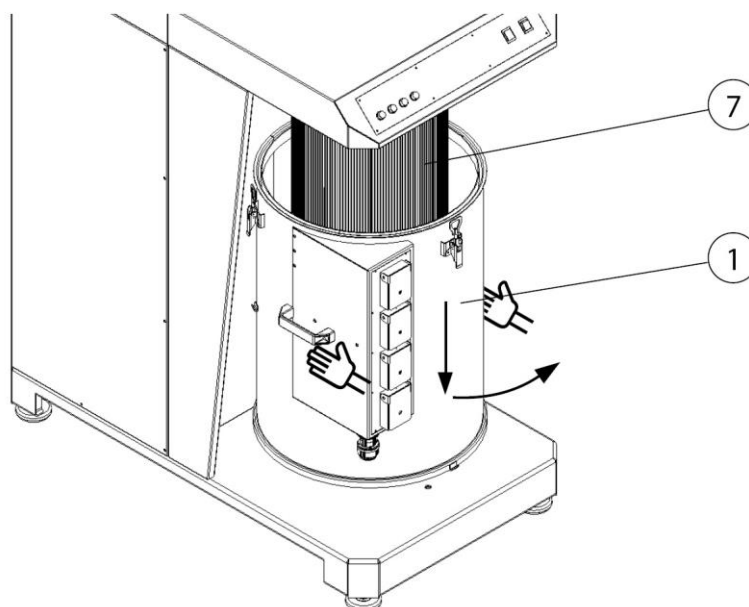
remplacement du filtre – démontage du boîtier de filtre
